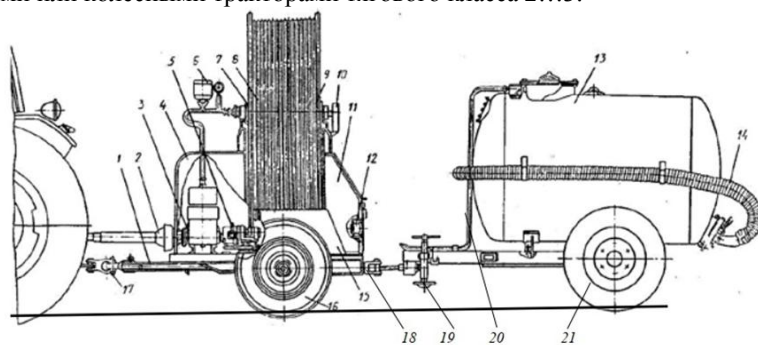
Прицепная дренапромывочная машина МР-18: 1-дышло; 2-карданный вал; 3-водяной насос; 4-капот; 5-редуктор; 6,7-барабан; 8, 9-высоконапорный шланг; 10, 12- тормоза; 11- ящик для инструментов; 13-
